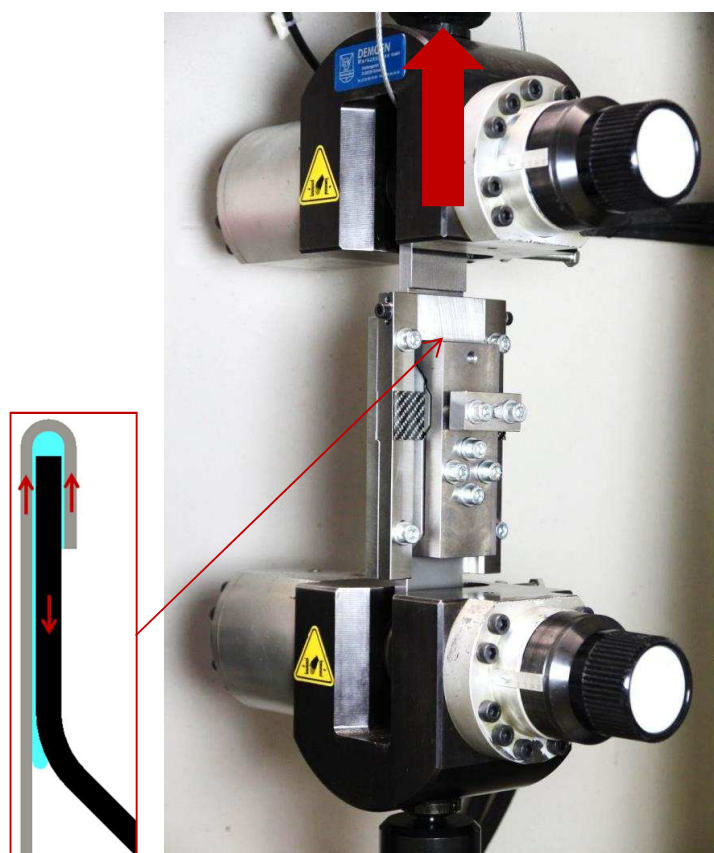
Tvar zkušební vzorku pro určení pevnosti lemového spoje s fixací [P11]
